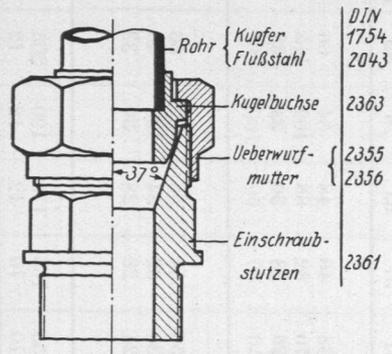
Einschraubverschraubung, schwer, nach DIN 2360.
